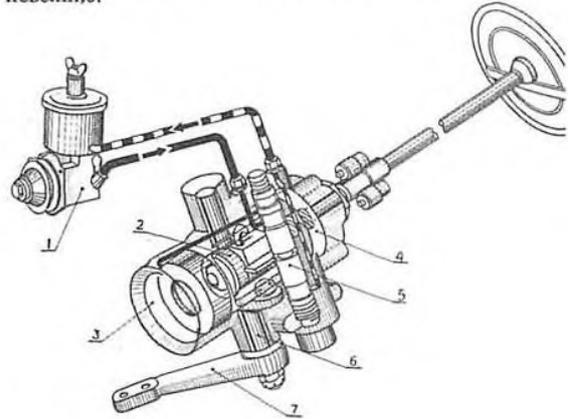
Рулевое управление легкового автомобиля «Даймлер-Бенц-300» выпуска 1962 года: 1 — насос с резервуаром; 2 — гайка рулевой передачи; 3 — рабочий поршень; 4 — червяк рулевой передачи; 5 — золотник управления; 6 — вал сошки руля; 7 — рулевая сошка.
